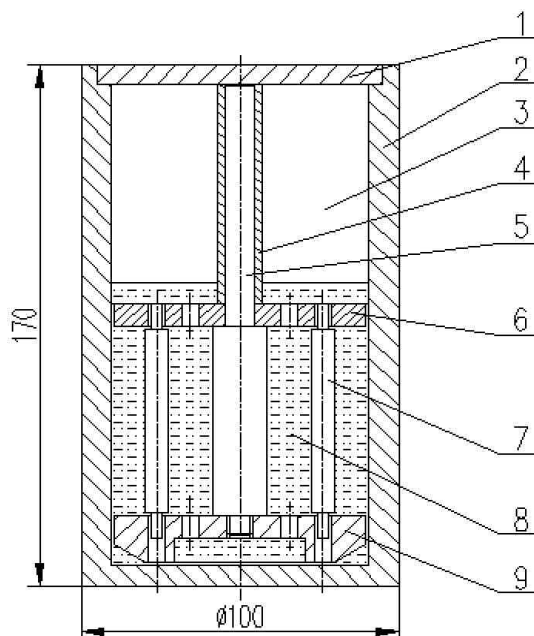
Контейнер для коррозионных испытаний: 1 – крышка контейнера; 2 – корпус контейнера; 3 – свободный объем для размещения поглотителя кислорода; 4 – втулка; 5 – шток; 6 – верхний держатель образцов; 7 – образец; 8 – жидкий свинец; 9 – нижний держатель образцов
